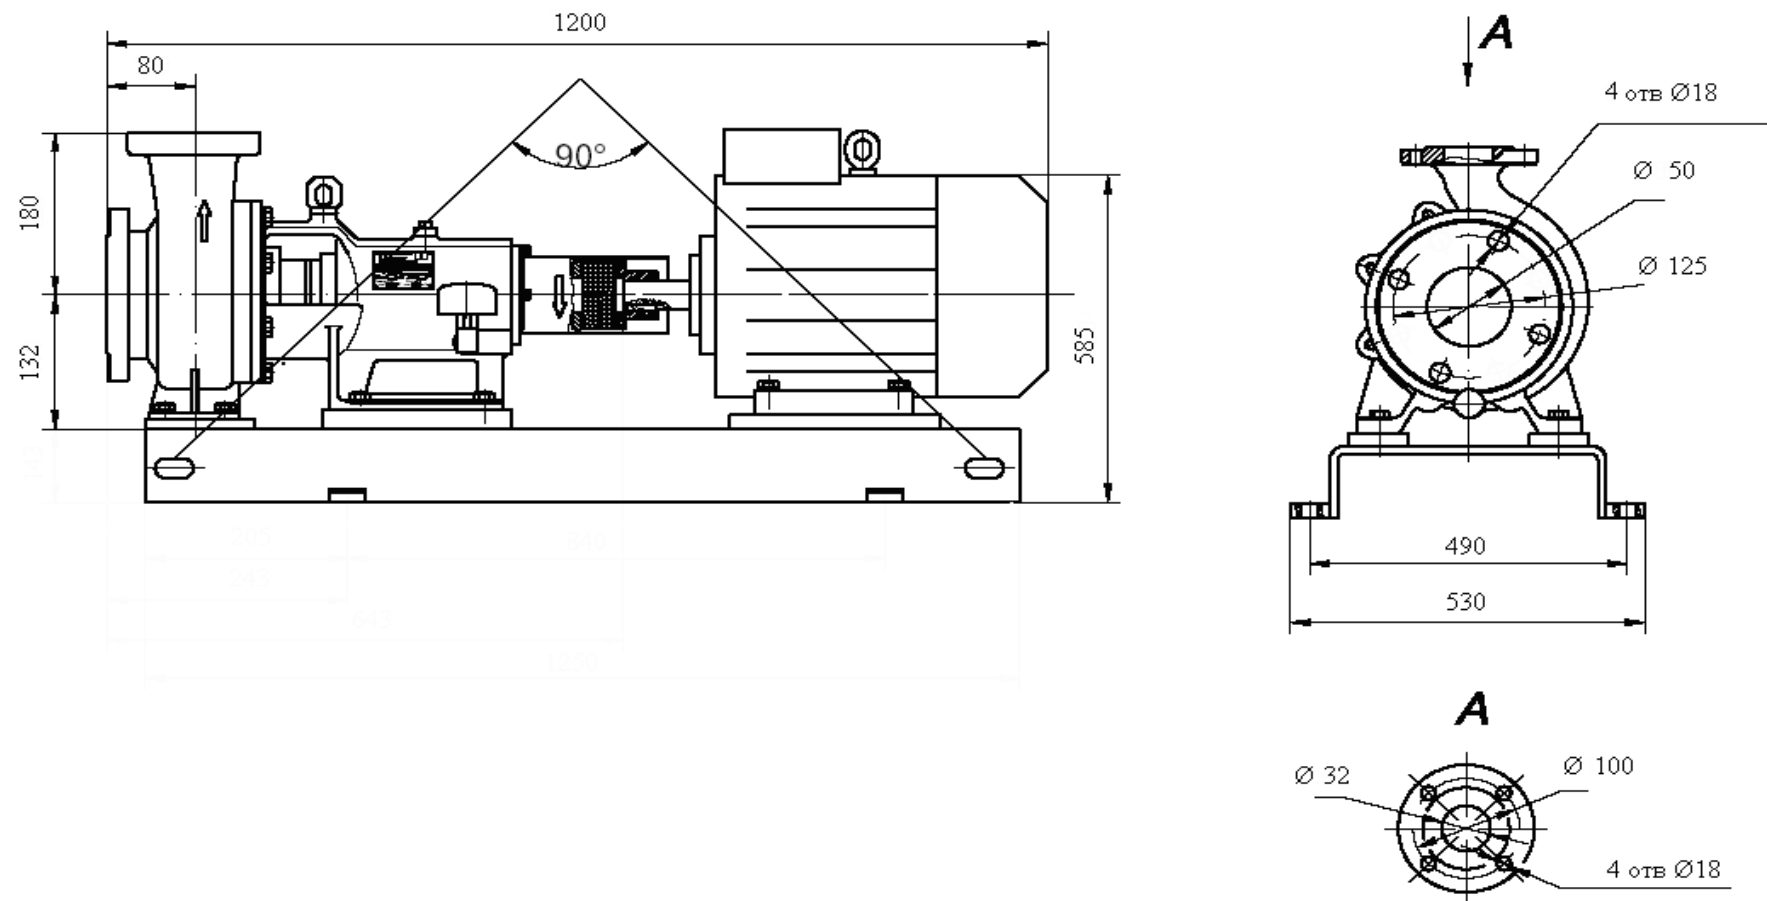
Габаритный чертеж насоса GMH10AP001
